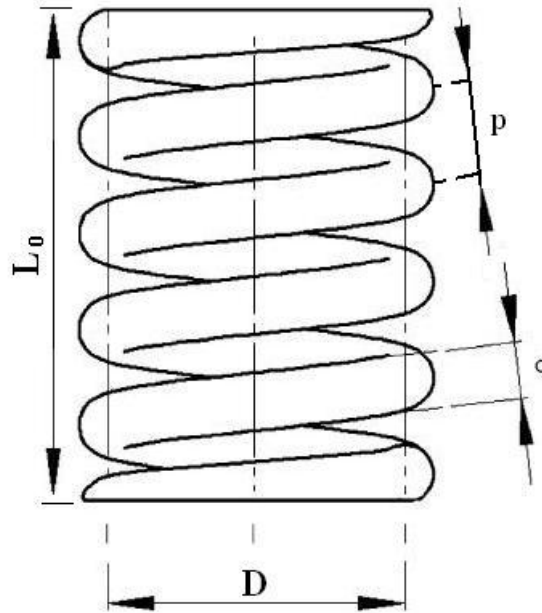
Dimensões de mola com seção circular e final plano esmerilhado [38].
